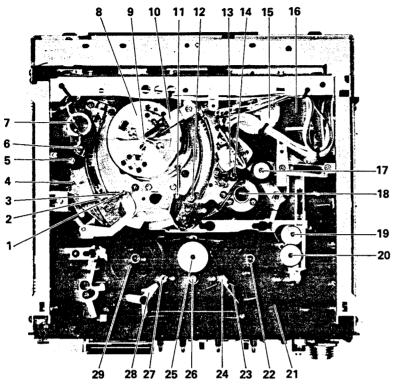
Draufsicht Fig. 1-4 Top view
